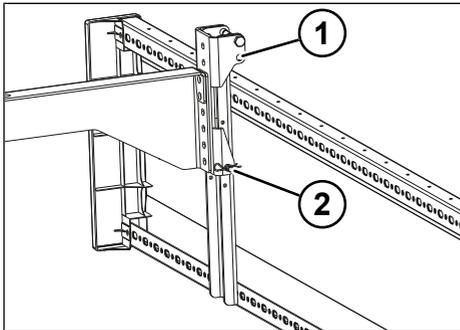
Dispositivo di protezione laterale abbassato (vista lato posteriore)
